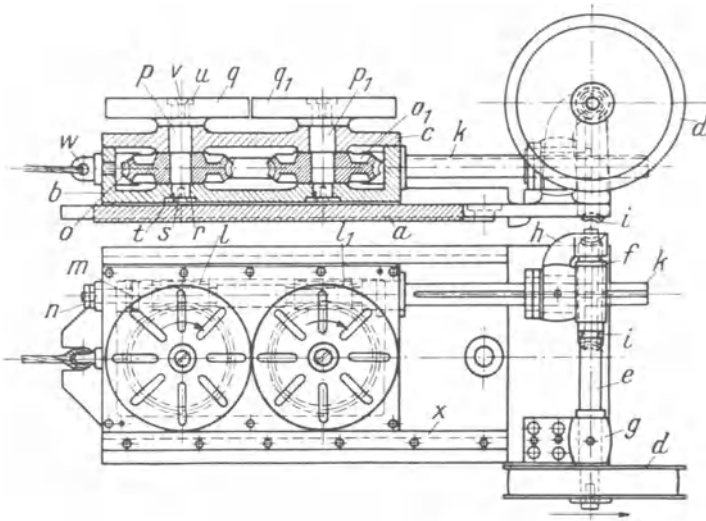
Kopier-Fräsvorrichtung für mannigfache Formen.
